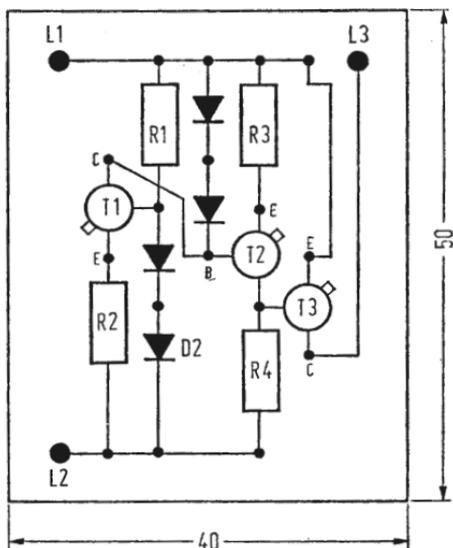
Montaggio del circuito di Fig. 4.02 visto dal lato dei componenti
